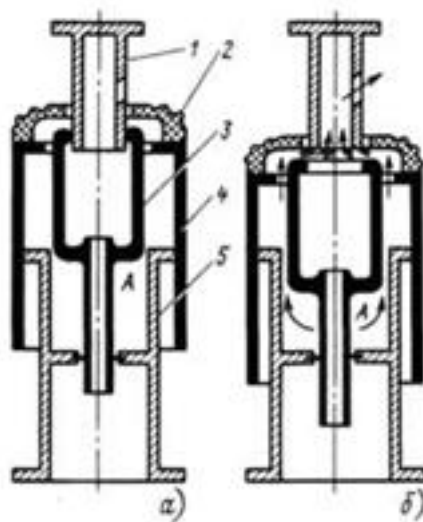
Автопневматическое дугогасительное устройство элегазового выключателя 110кВ
